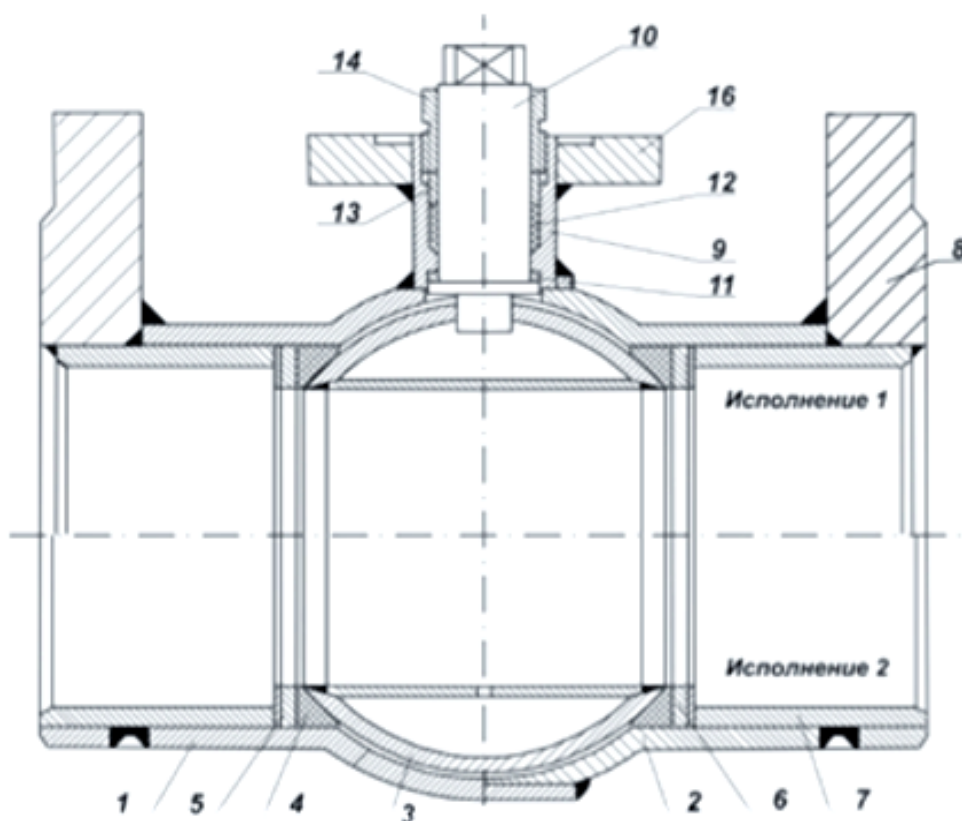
Штамповсварной шаровой кран в двух исполнениях: 1 и 2 – полукорпуса, 3 – шаровая пробка, 4 – седла, 5 – опорные кольца, 6 – пружинные шайбы, 7 – упоры, 8 – фланцы, 9 – корпус штока, 10 – шток, 11 – опорное кольцо, 12 – уплотнительное кольцо, 13 – нажимная втулка, 14 – резьбовая втулка, 15 – рукоятка, 16 – малый фланец
